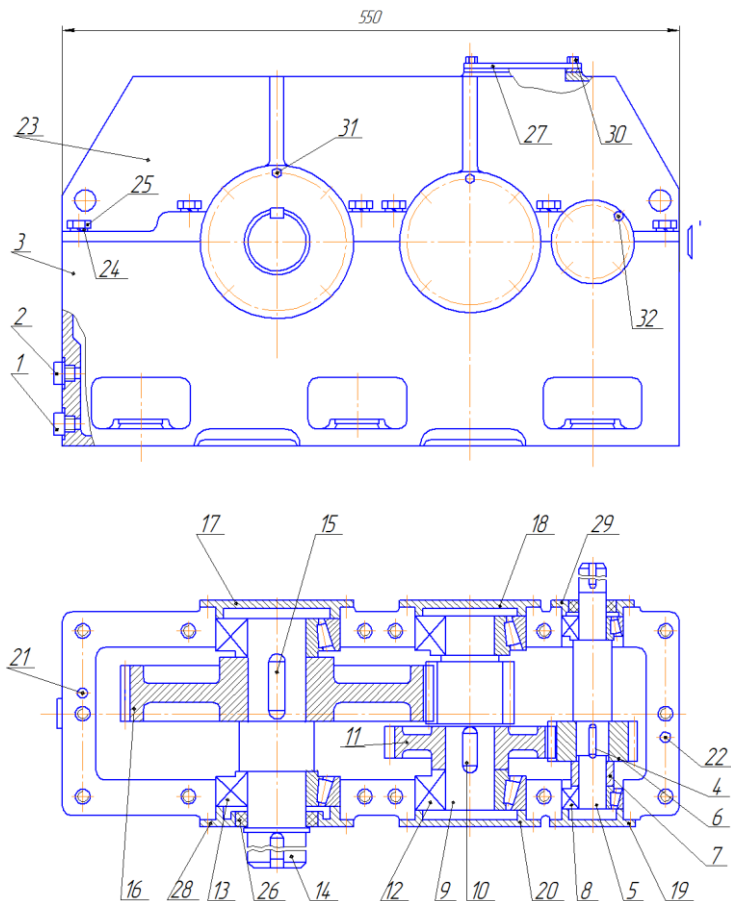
Редуктор двоступінчастий циліндричний Ц2У-400Н
